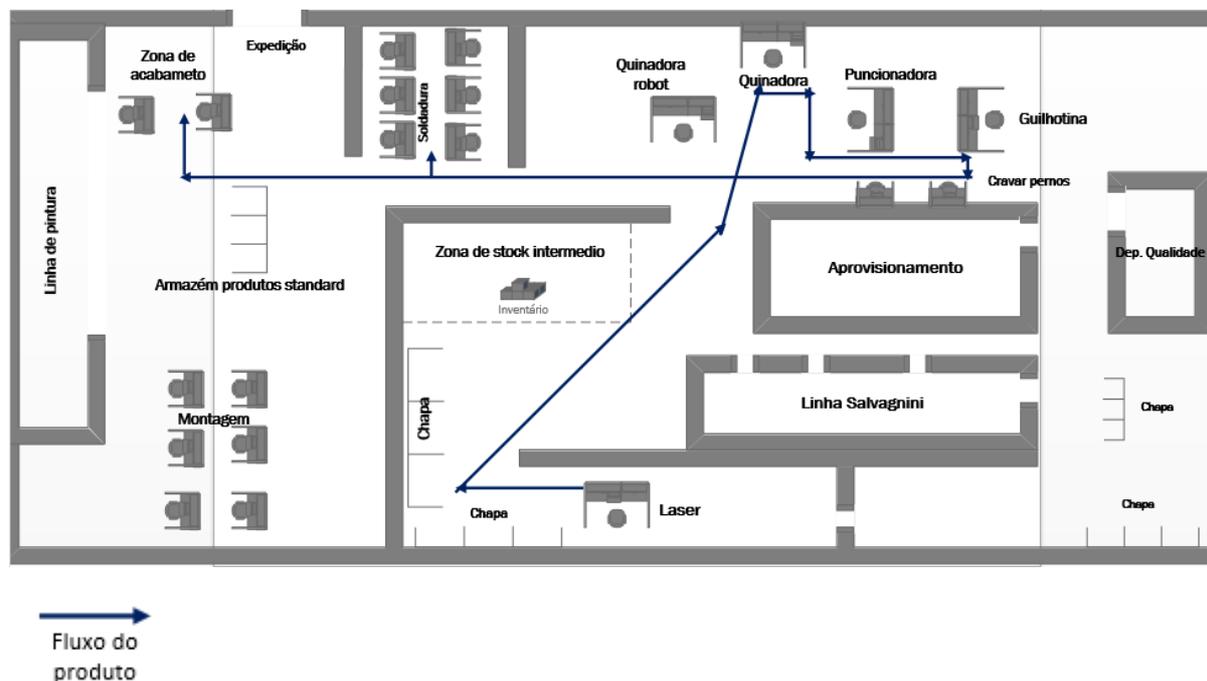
Processo de fabrico de um painel para a Microprossedadora (Laser-Quinagem-Pernos-soldadura-acabamento).
